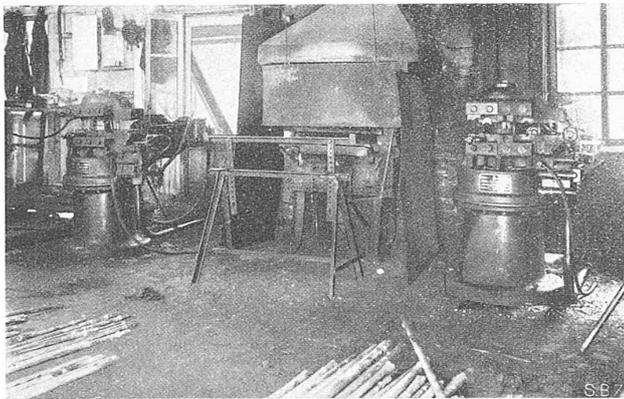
„Ingersoll-Rand“-Bohrer-Schmiedemaschinen.
